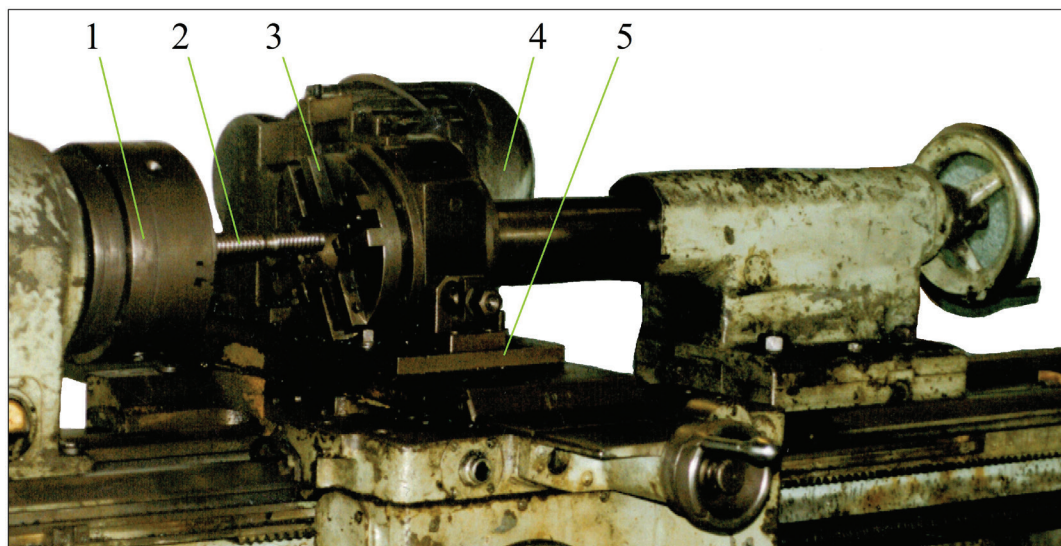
Приспособление для нарезания резьбы охватывающей фрезой:
